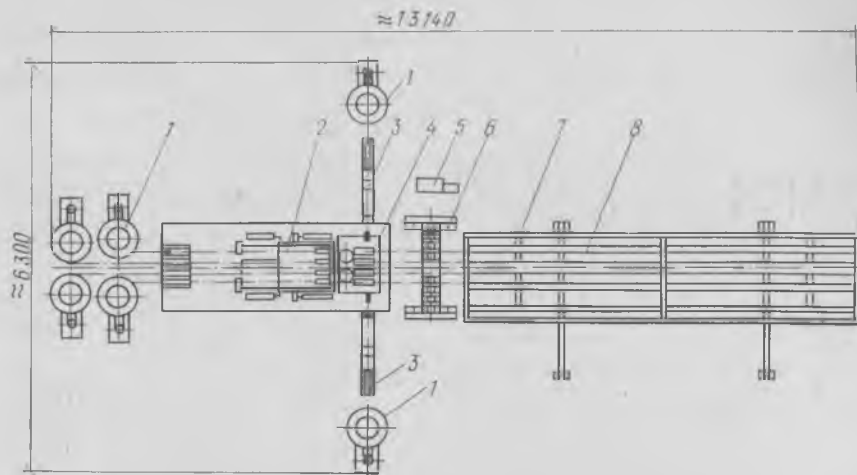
Автоматическая линия для сварки двух плоских двухветвевых каркасов
